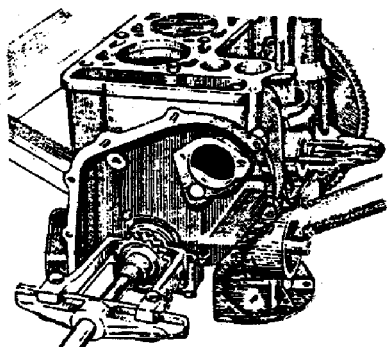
Remoção da engrenagem da árvore de manivelas
